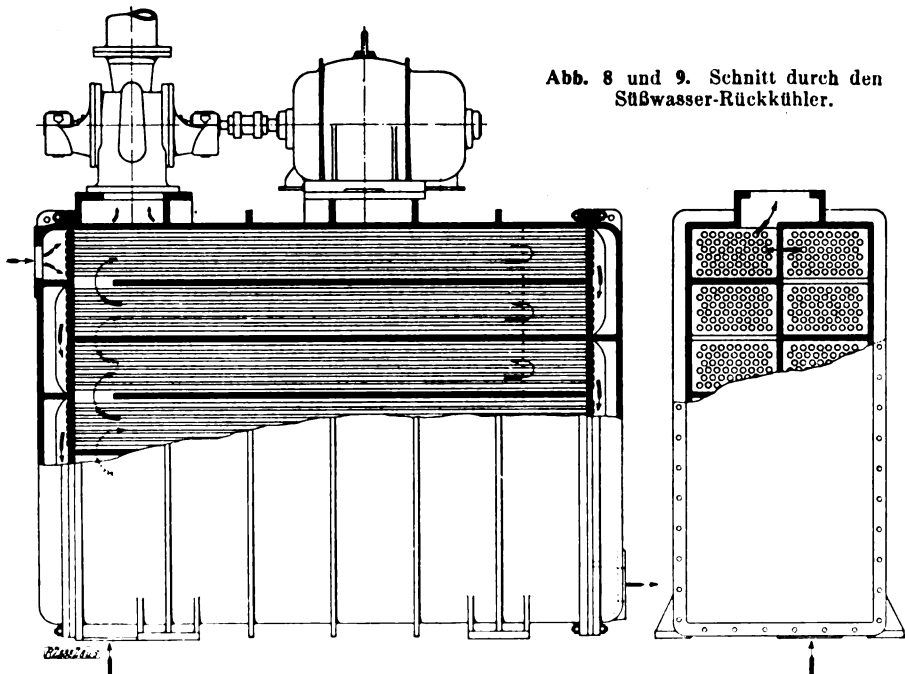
und 9. Schnitt durch den Süßwasser-Rückkühler.
